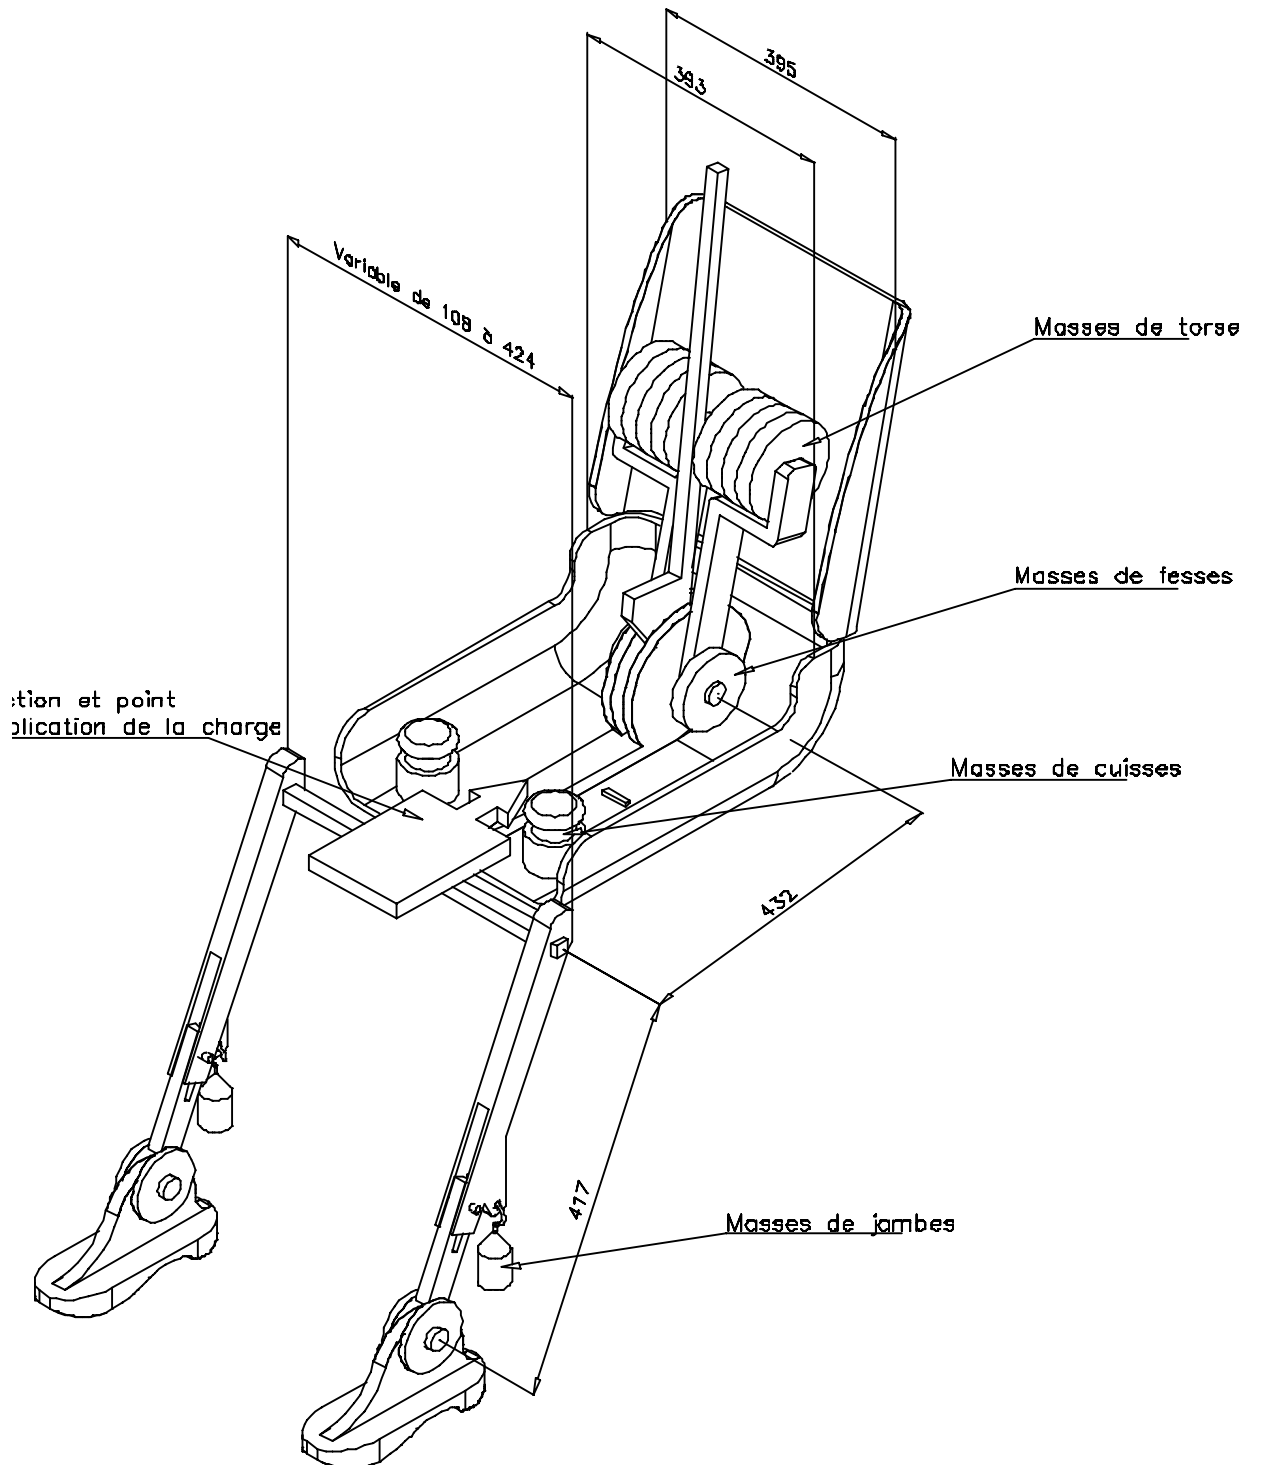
Dimensions des éléments de la machine 3 DH et emplacement des masses
